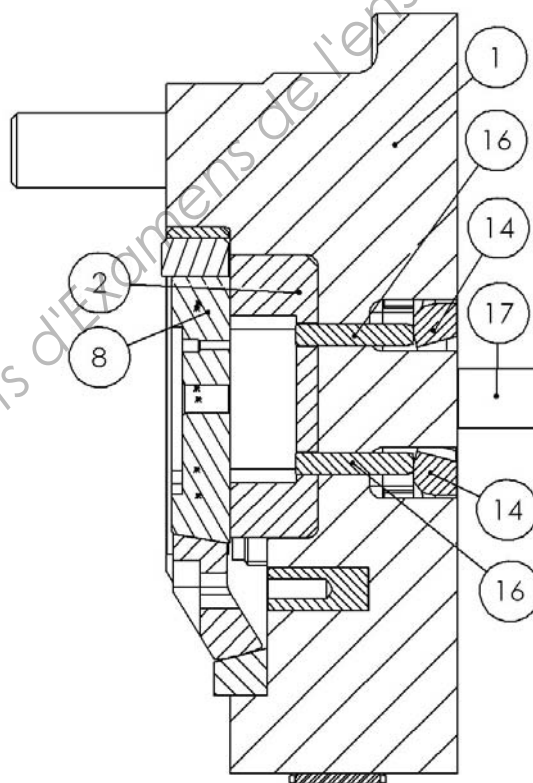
Coupe longitudinale LL (repérée sur figure 2)
